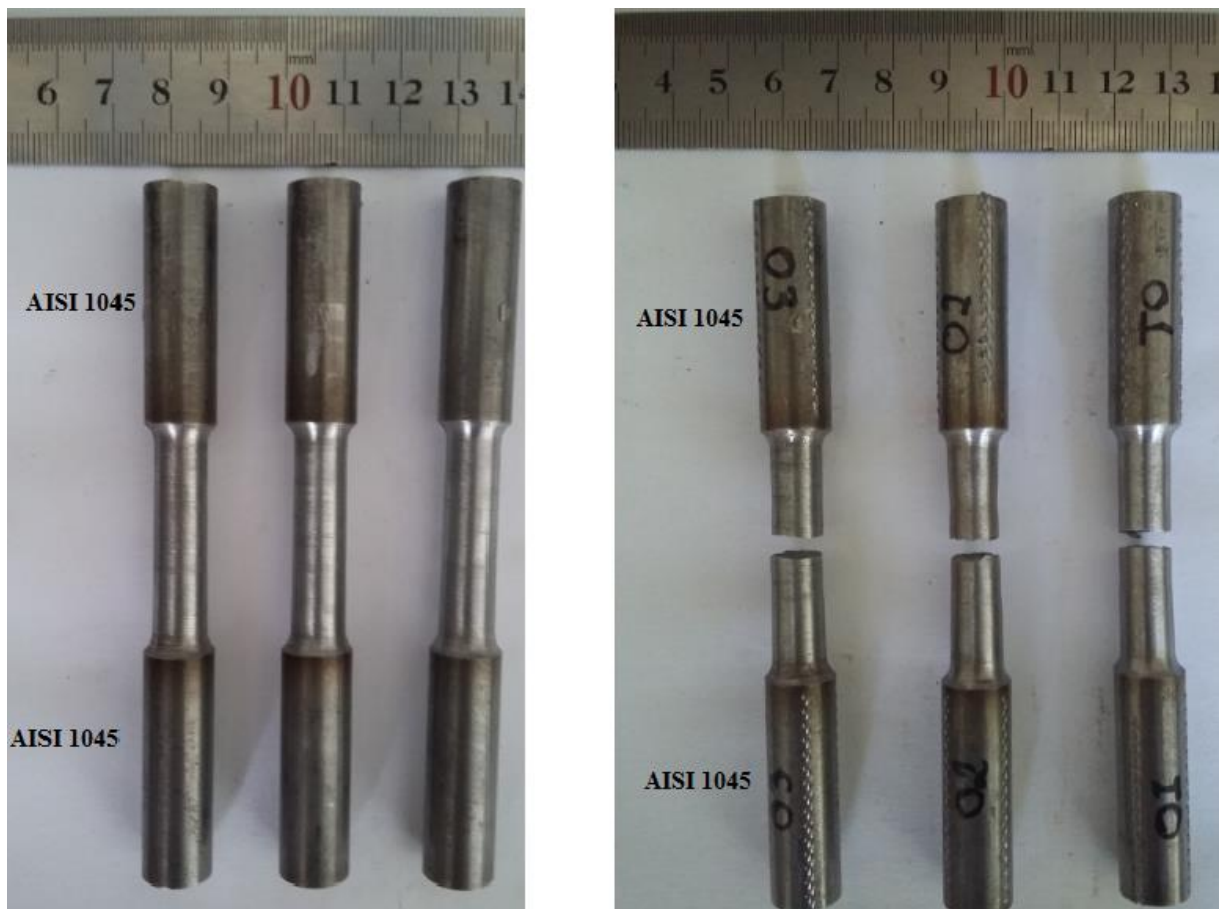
Corpo de prova 22; 3-2-1. Soldagem similar do aço ASTM 1045 e ensaio de tração
